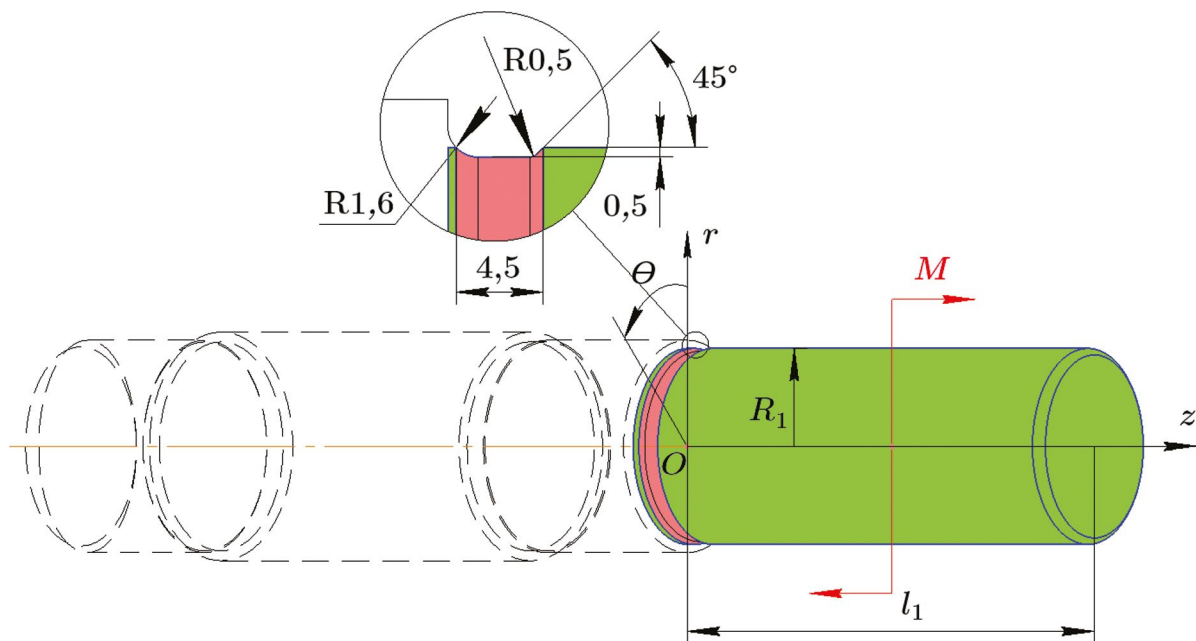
Расчетная схема поверхностно упрочненного цилиндрического образца с канавкой, представляющего часть ступенчатого вала
